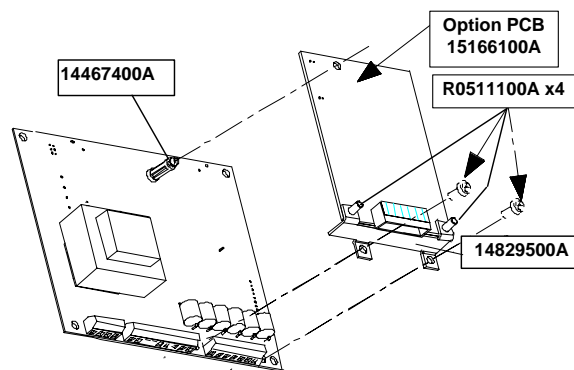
Montando la PCB PROFIBUS opcional en el gabinete de montaje en panel
